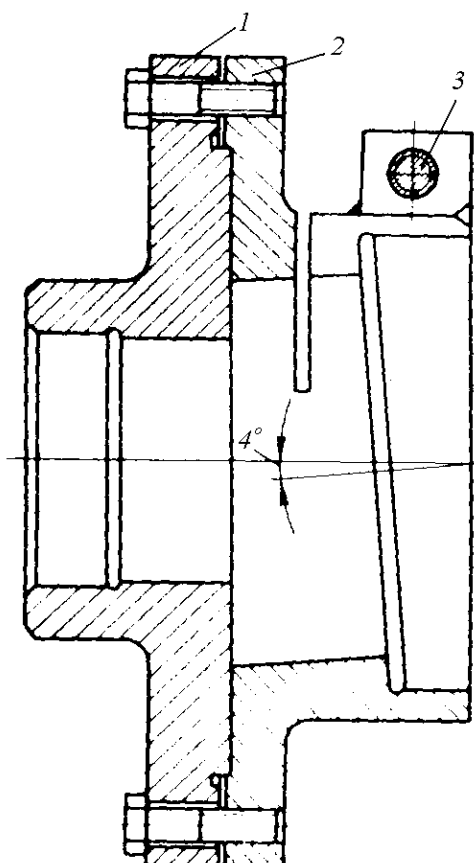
Приспособление для проточки уплотнительных поверхностей седел задвижки.
